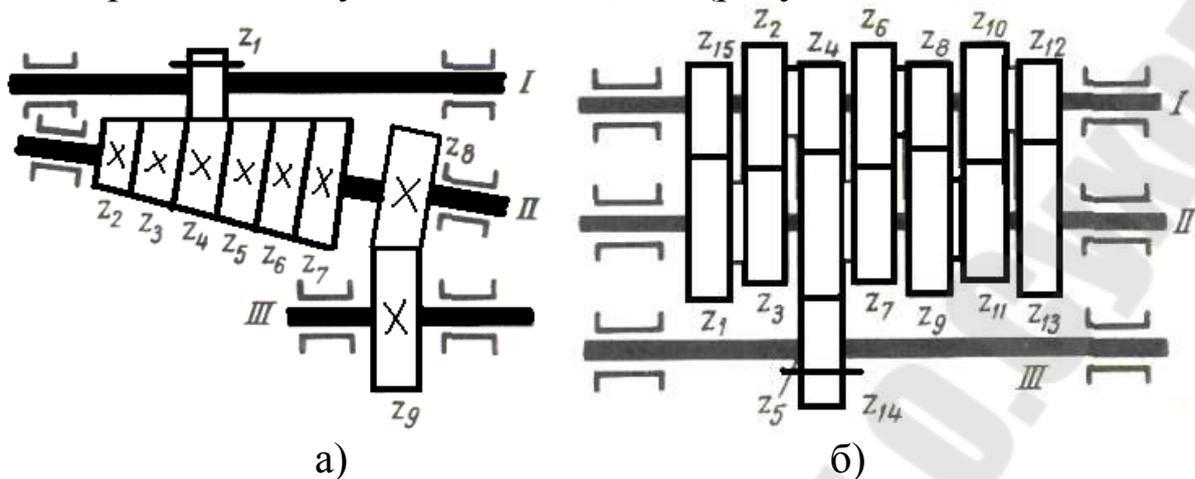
Схема коробок передач с передвижной зубчатой шестерней
